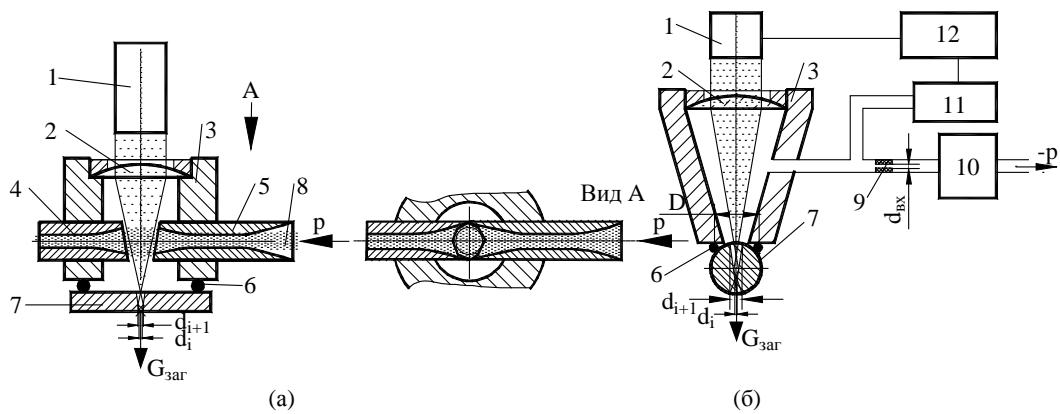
Схемы ЛТУ с устройствами для контроля текущего размера отверстия по расходу воздуха через его сечение. (1 – лазер; 2 – линза; 3 – корпус (камера); 4 – сопло приемное; 5 – сопло напорное; 6 – уплотнение; 7 – заготовка; 8 – воздух; 9 – дроссель; 10 – вакуум-насос; 11 – датчик давления; 12 – блок питания лазера).
